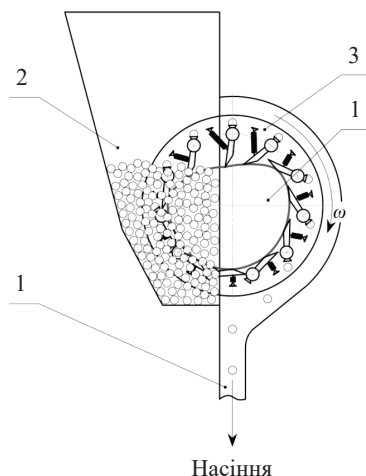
Схема висівного пневмомеханічного апарата дозатором направленої дії (вид збоку): 1 — нерухомий копір; 2 — насіннева камера; 3 — висівний диск; 4 — насіннєпровід
